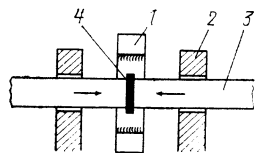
Принцип сварки: 1 — переносная кольцевая горелка; 2 — зажимное и центрирующее устройство (с помощью пружины); 3 — изделие (труба); 4 — промежуточная вставка
